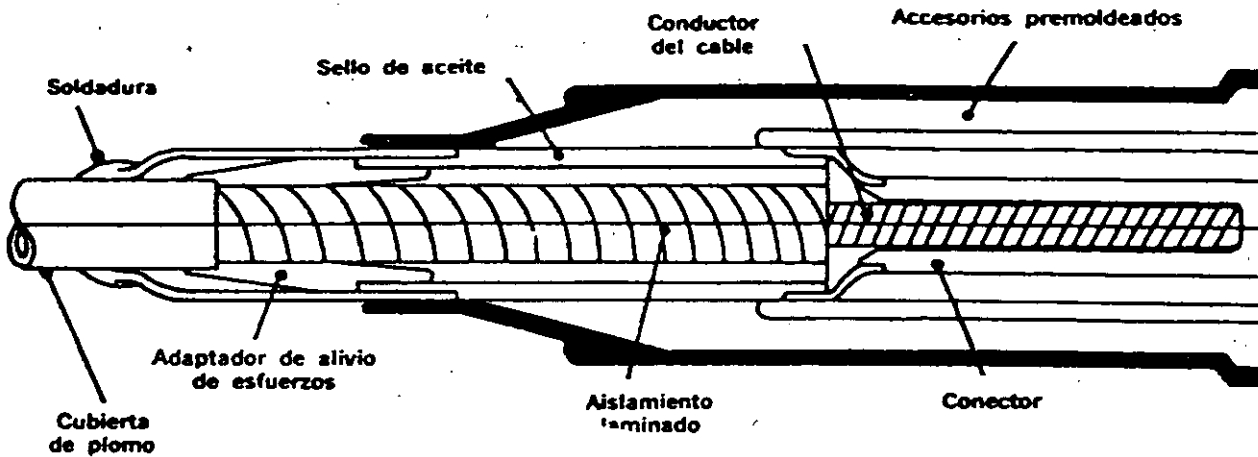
Empalme premoldeado para cable con aislamiento laminado.
